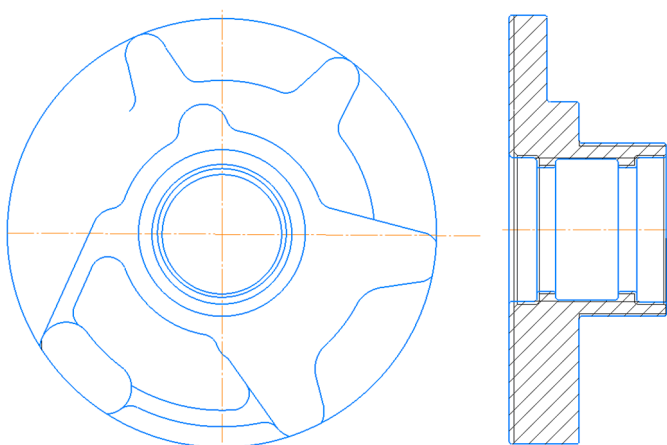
Ескіз деталі «Стакан підшипниковий»
